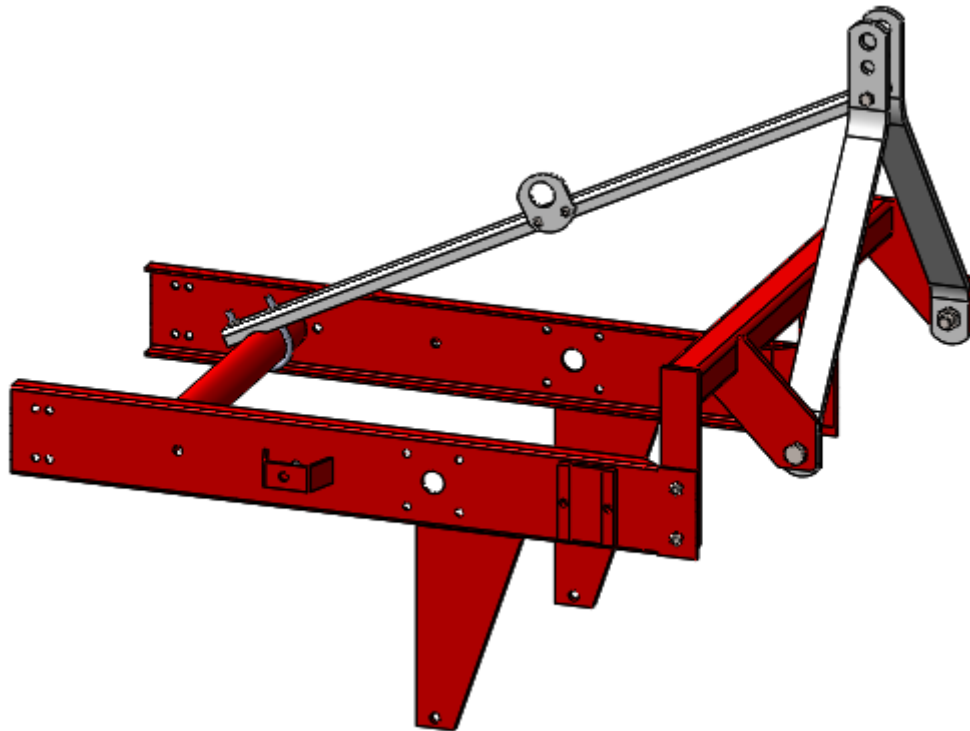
Vue en perspective du châssis sur SolidWorks
